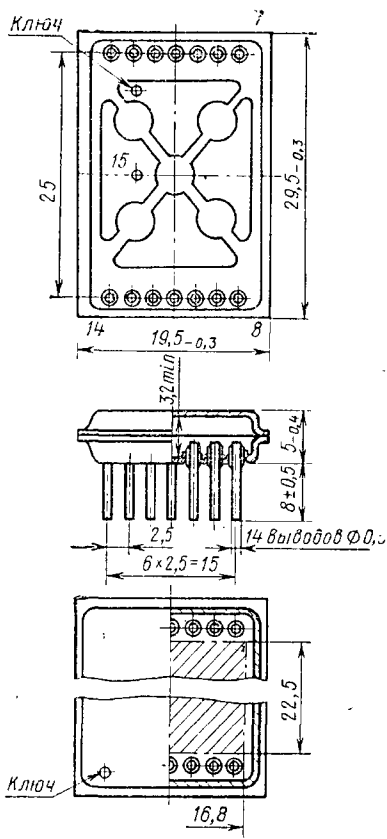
Конструкция металлостеклянного корпуса 1207 (155.15-1)
